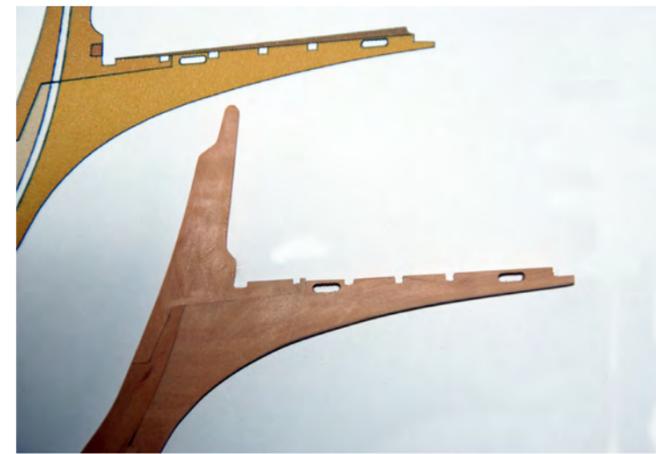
Premier plan du taille-mer. Les entailles et les losanges sont bien visibles.
